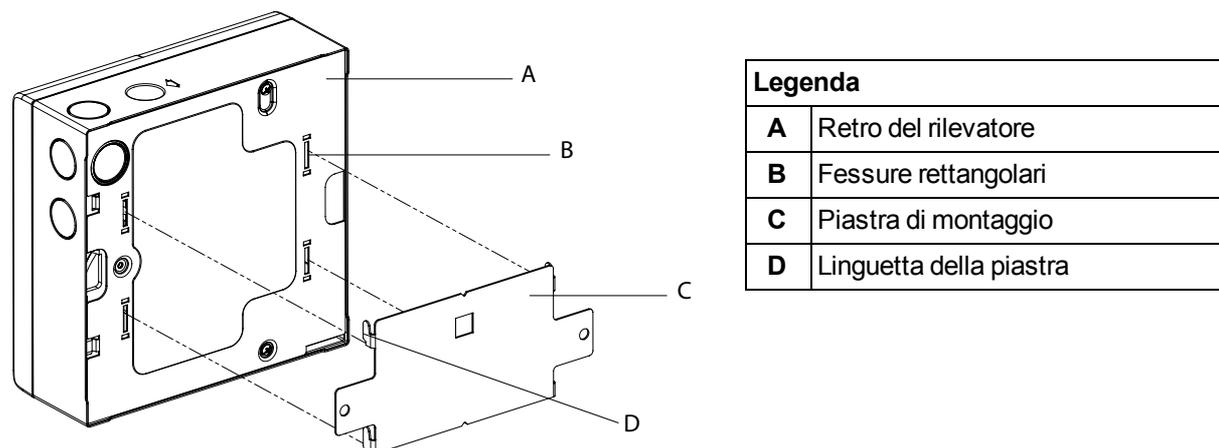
Installazione del Rilevatore sulla piastra di montaggio
